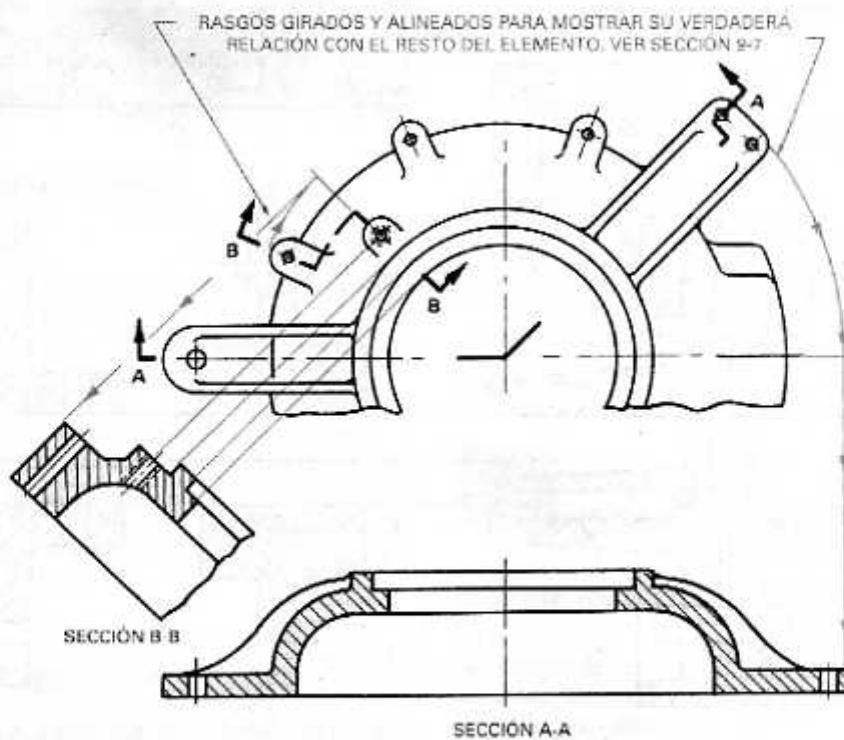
Posicionamiento de secciones por plano paralelo al eje.
